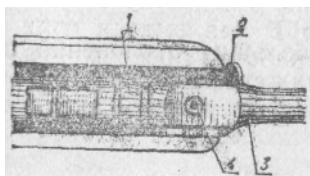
Пулеприемник пневматической винтовки «311» (ГДР):
